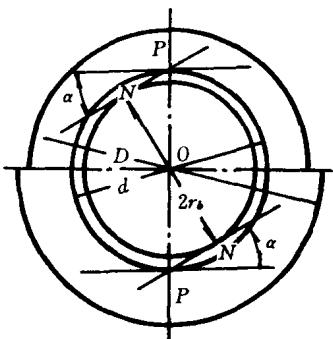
标准齿轮和变位齿轮的顶圆、根圆和极限啮合点
